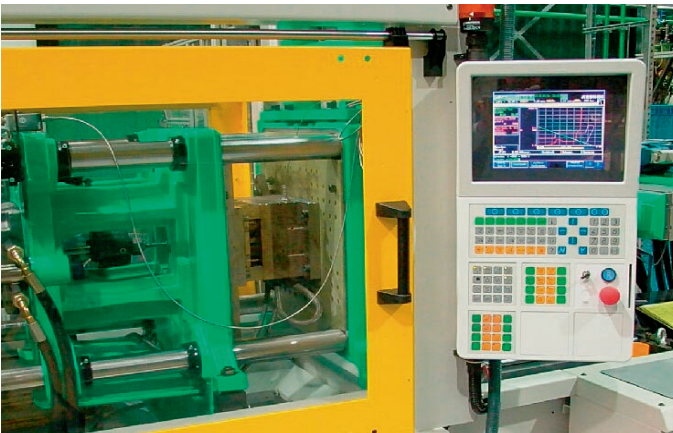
Spritzgießmaschine mit Präzisionswerkzeug
